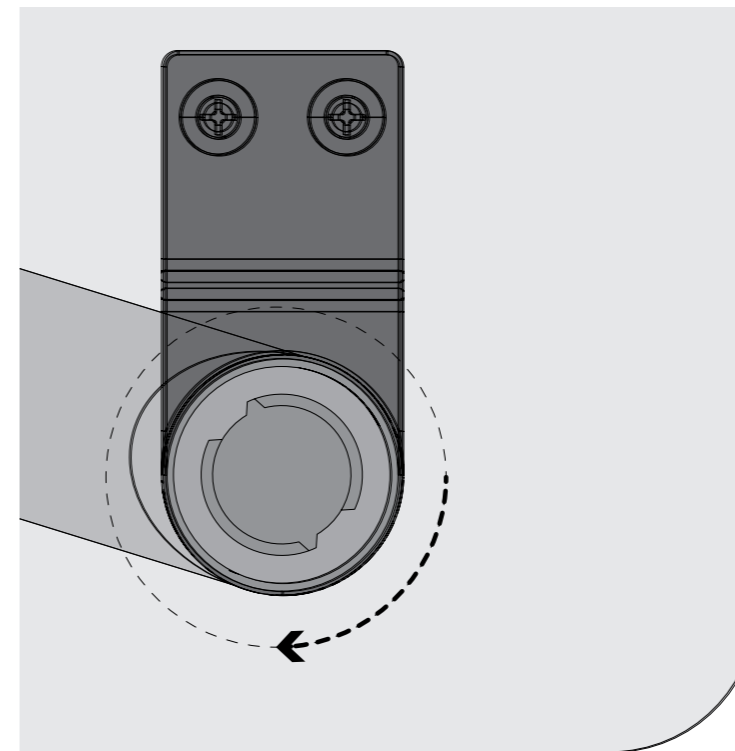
Sistema a baionetta per la connessione del piano al telaio del banco KJ01.
